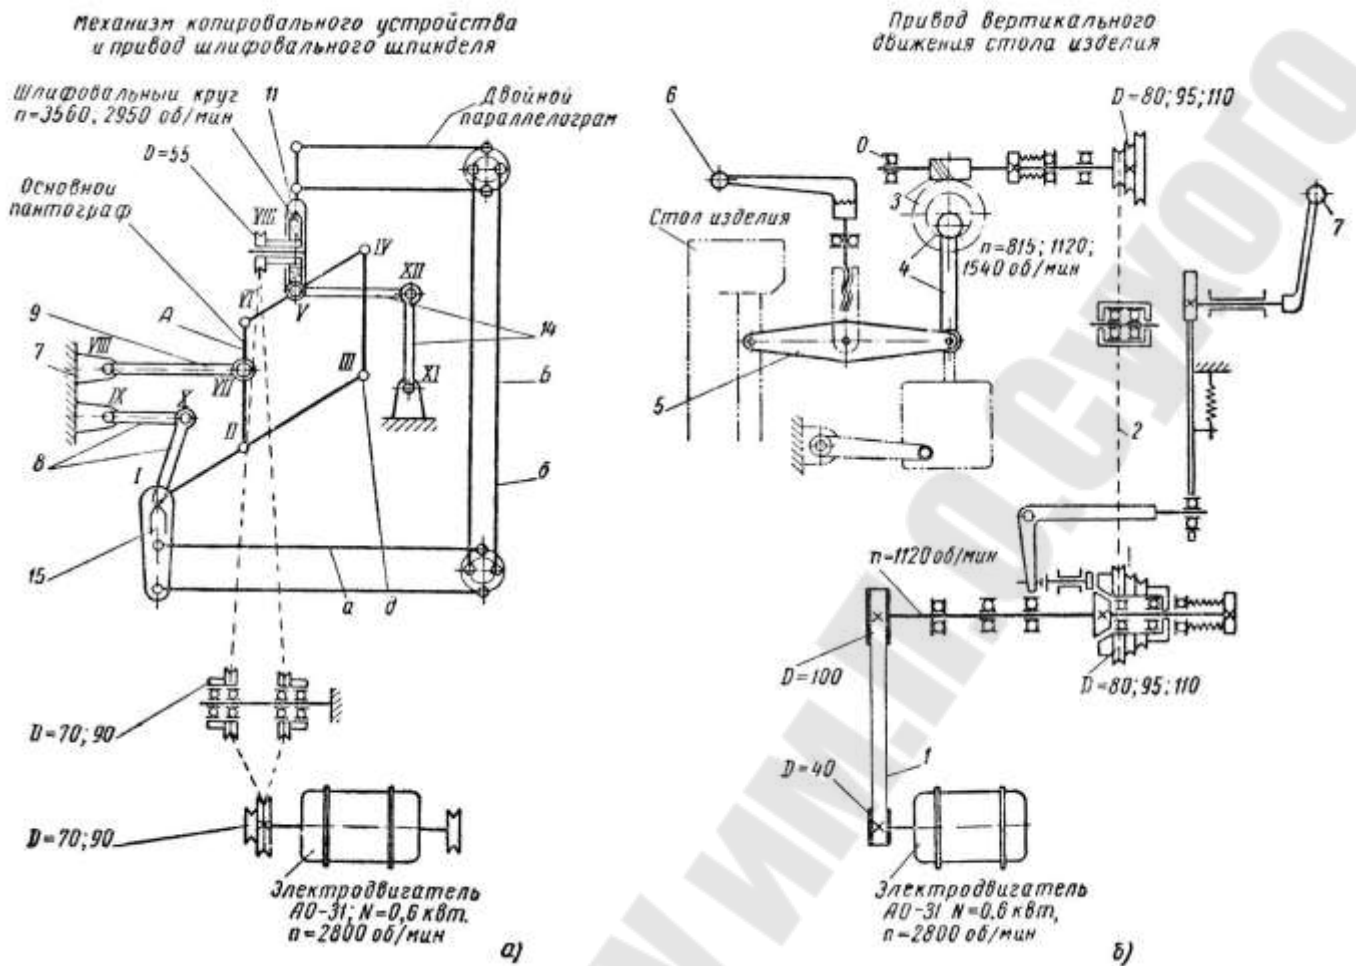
Принципиальная схема профилешлифовального станка модели Ш-228
